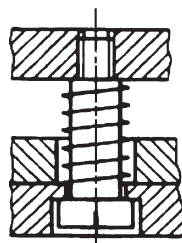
Сборочный чертеж стандартного элемента конструкции
